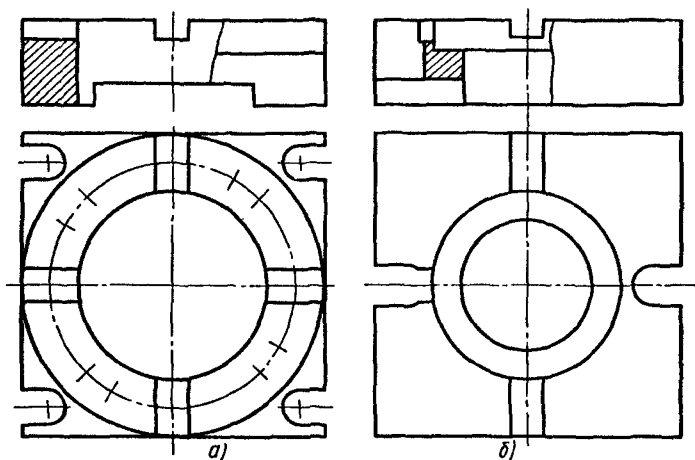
Детали для фиксации и закрепления пуансонов и матриц:
